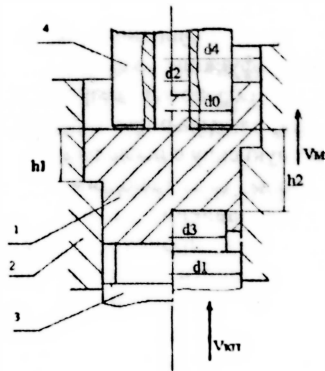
Схема изготовления двухполостной детали с фланцем и отростком способом комбинированного выдавливания
